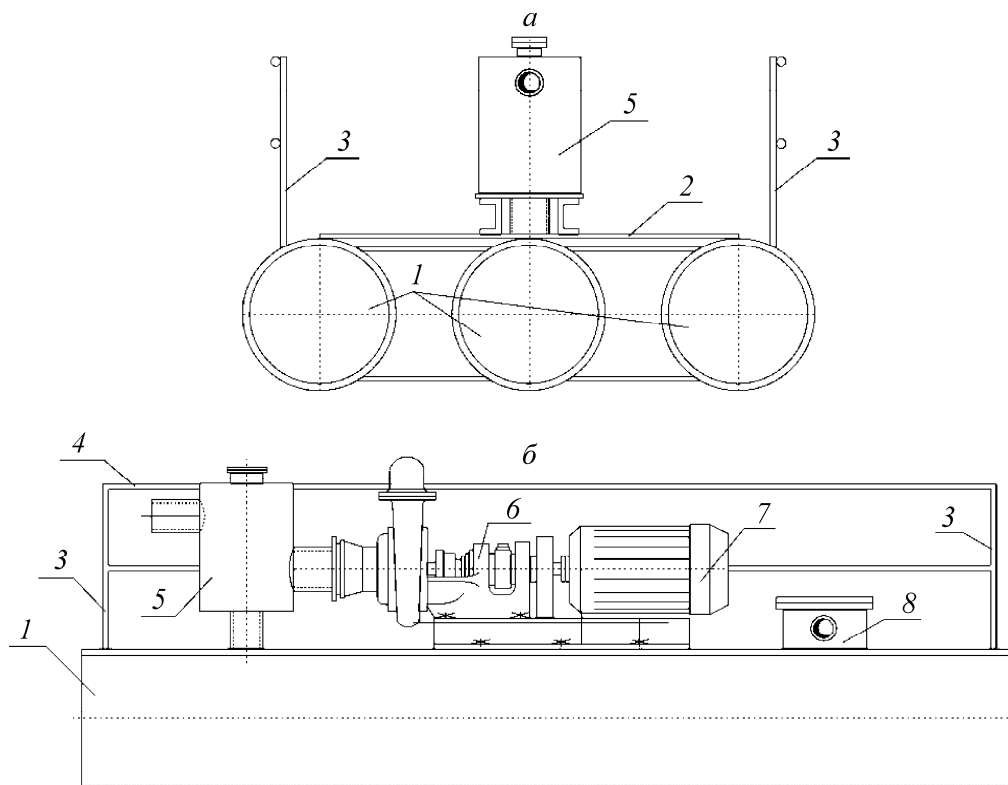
Плавающая водоотливная установка *a* (вид с торца): 1 — металлические трубы-поплавки; 2 — палубный настил; 3 — ограждения; 4 — поручни; 5 — бак-запасник воды; *б* (вид сбоку): 6 — насос; 7 — электродвигатель; 8 — ящик для кабеля
